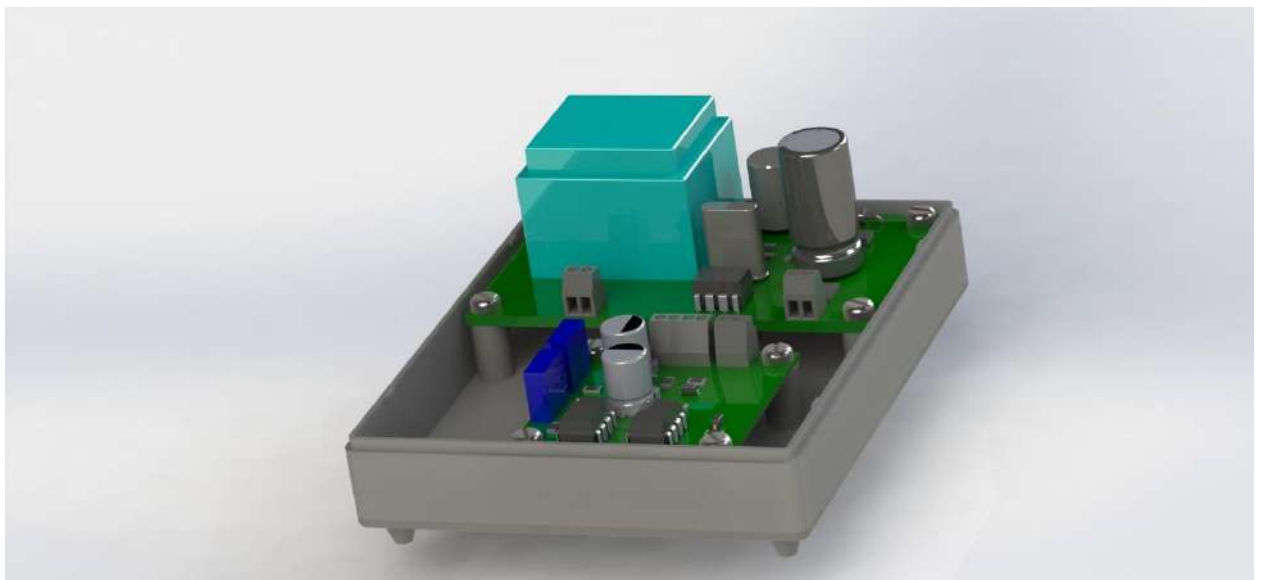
Розташування друкованого вузла в корпусі
